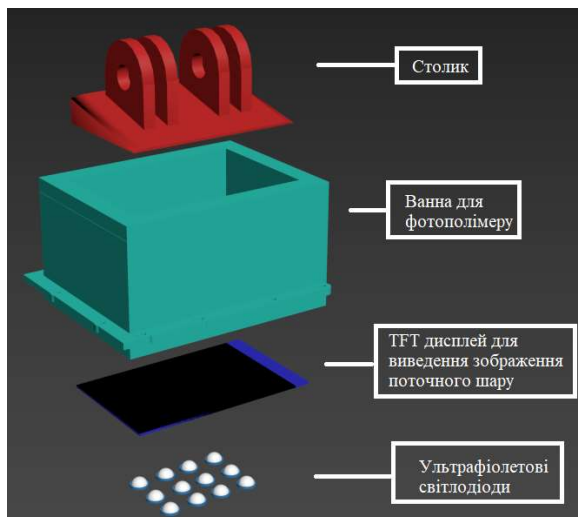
Компоненти конструкції фотополімерного 3д принтер
